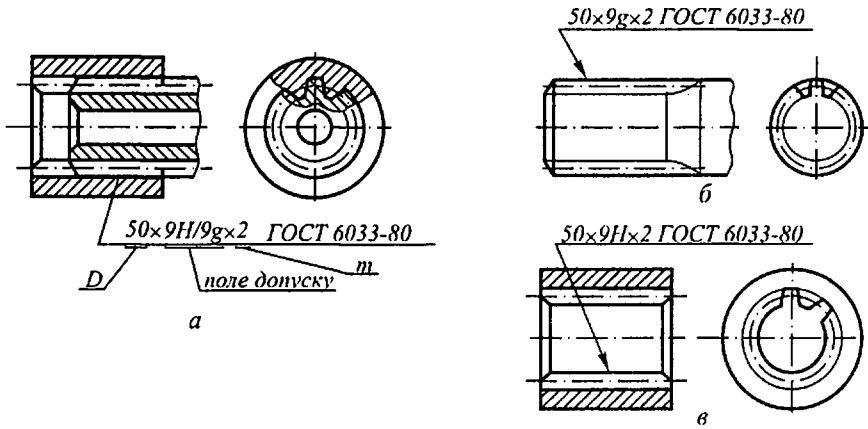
Позначка шліцевого з'єднання з евольвентними зубцями
